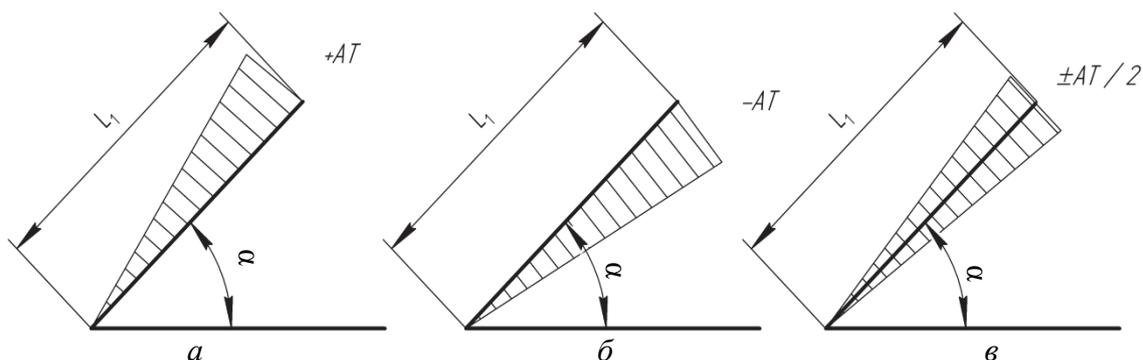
Схемы расположения полей допусков угловых размеров:
